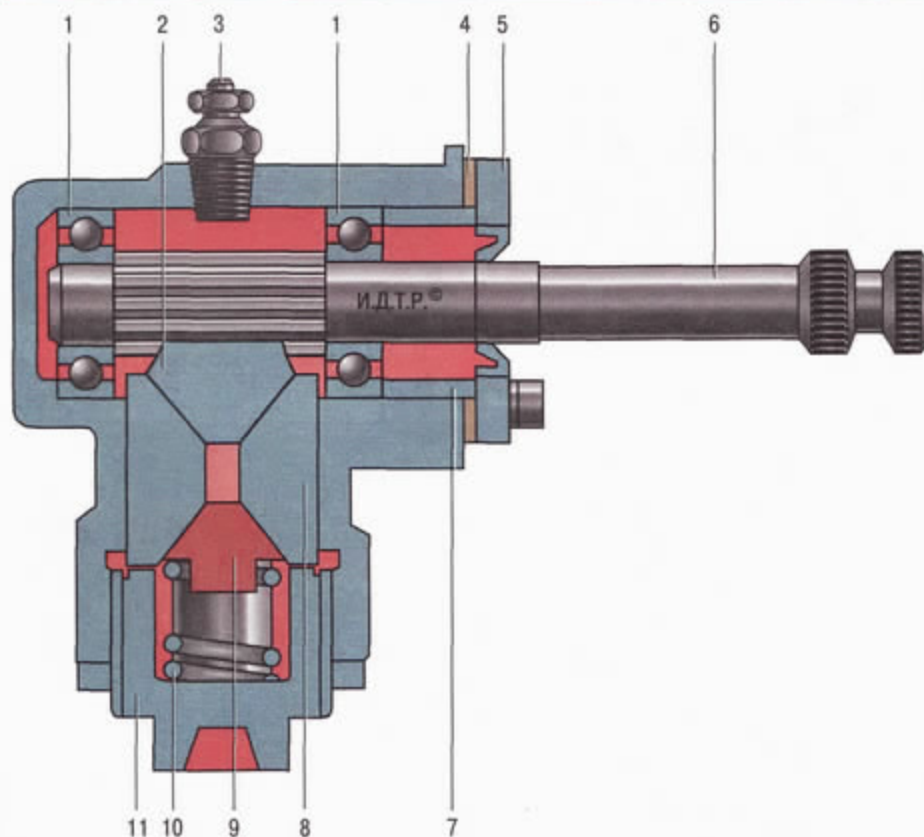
Устройство рулевого механизма: 1 – шариковый подшипник; 2 – рейка; 3 – сапун; 4 – регулировочная прокладка; 5 – крышка; 6 – вал-шестерня; 7 – распорная втулка; 8 – упор рейки; 9 – подпятник; 10 – пружина; 11 – регулировочная пробка
